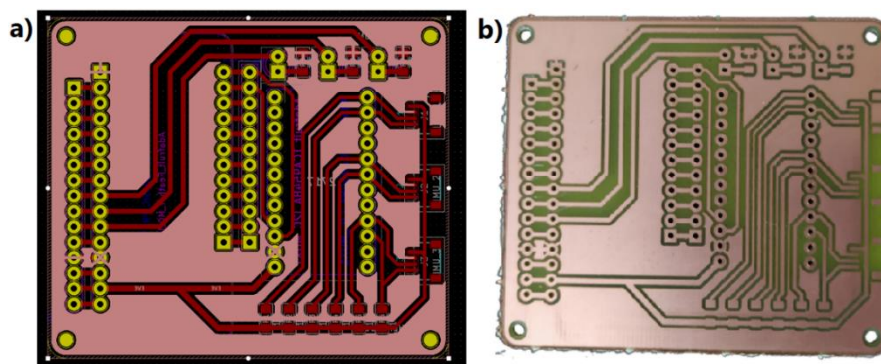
Tarjeta PCB para el sistema de tres IMU. A) Diseño en interfaz de huellas de KiCad. B) Resultado de fabricación de la tarjeta PCB.
